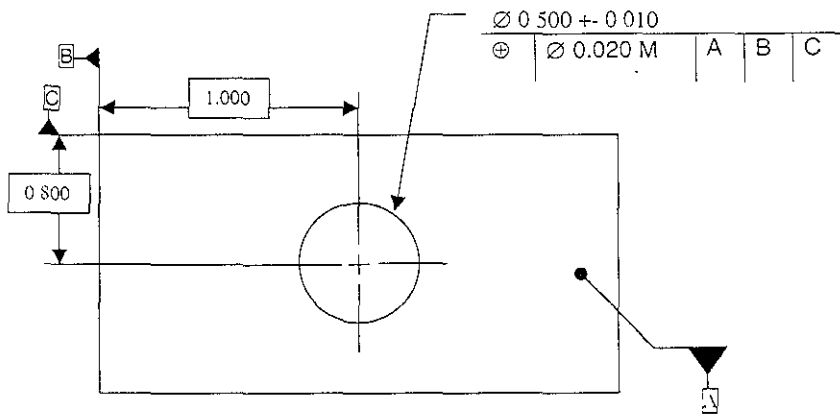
comp Completos para un dibujo con dimensiones y tolerancias geométricas
